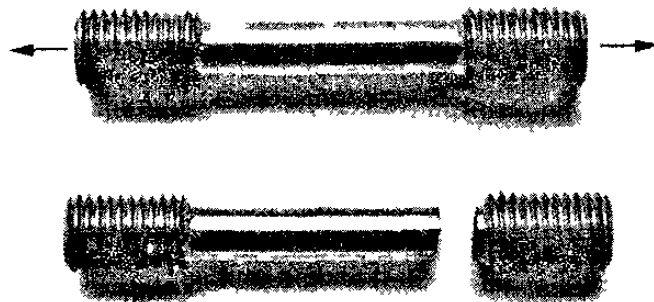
Probeta de fundición de hierro frágil de ensayo a la tensión
